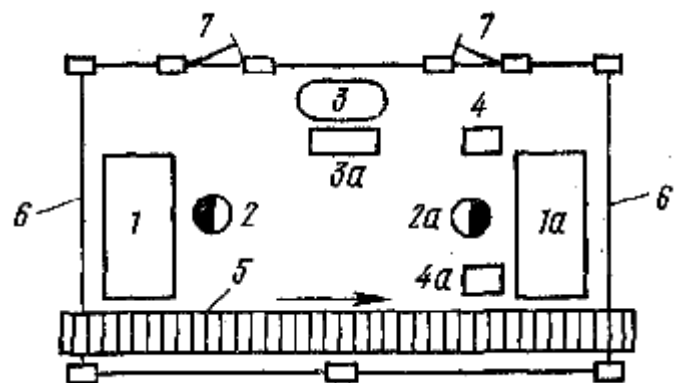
Кабіна для ручного дугового зварювання дрібних складальних одиниць поза потоком: 1 – стіл для складання і зварювання; 2 – стілець зварника; 3 – зварювальний трансформатор; 4 – щиток з рубильником; 5 – складське місце для деталей, що підлягають зварюванню; 5а – те ж, для зварених складальних одиниць; 6 – ящик з електродами; 6а – урна для залишків електродів; 7 – стіни кабіни на висоті 50...2000 мм; 7а – брезентові завіски
